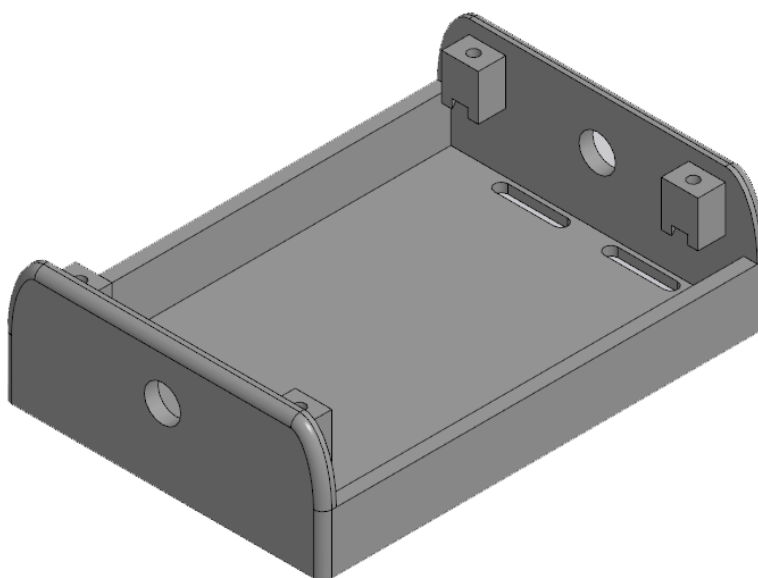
3D-модель корпусу акумуляторів
